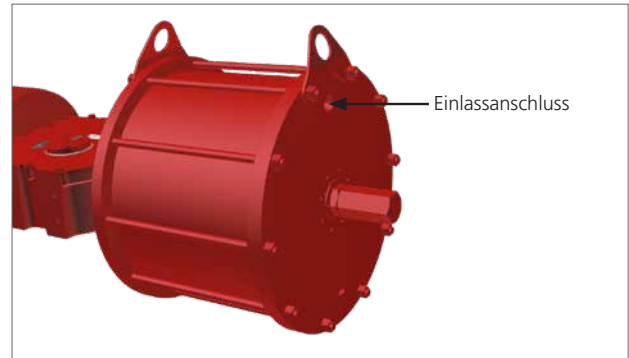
Einlassanschluss für einfach wirkenden Stellantrieb
